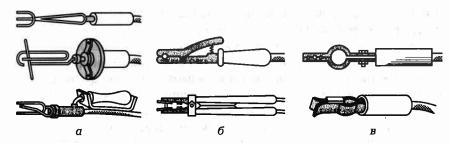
Электрододержатели для ручной дуговой сварки:
